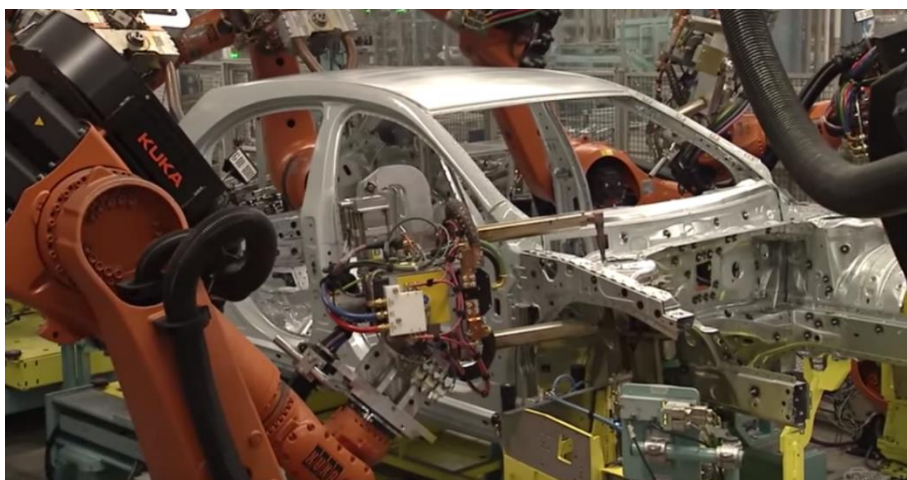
Le soudage par point robotisé dans l'industrie d'automobile
